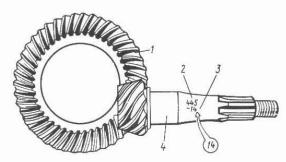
Piñones de ataque y conducido del engranaje de ángulo:
